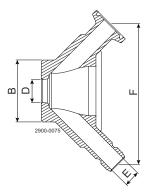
Cuerpo de la válvula: Depósito (para soldar)
